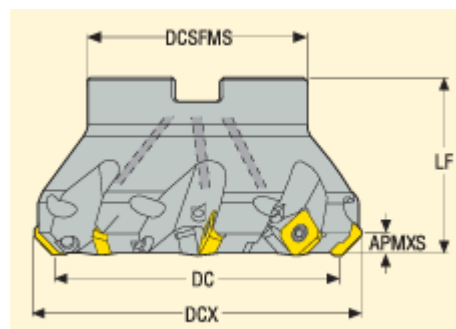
Фреза R220.53-8250-09-16C [12, с.137]
